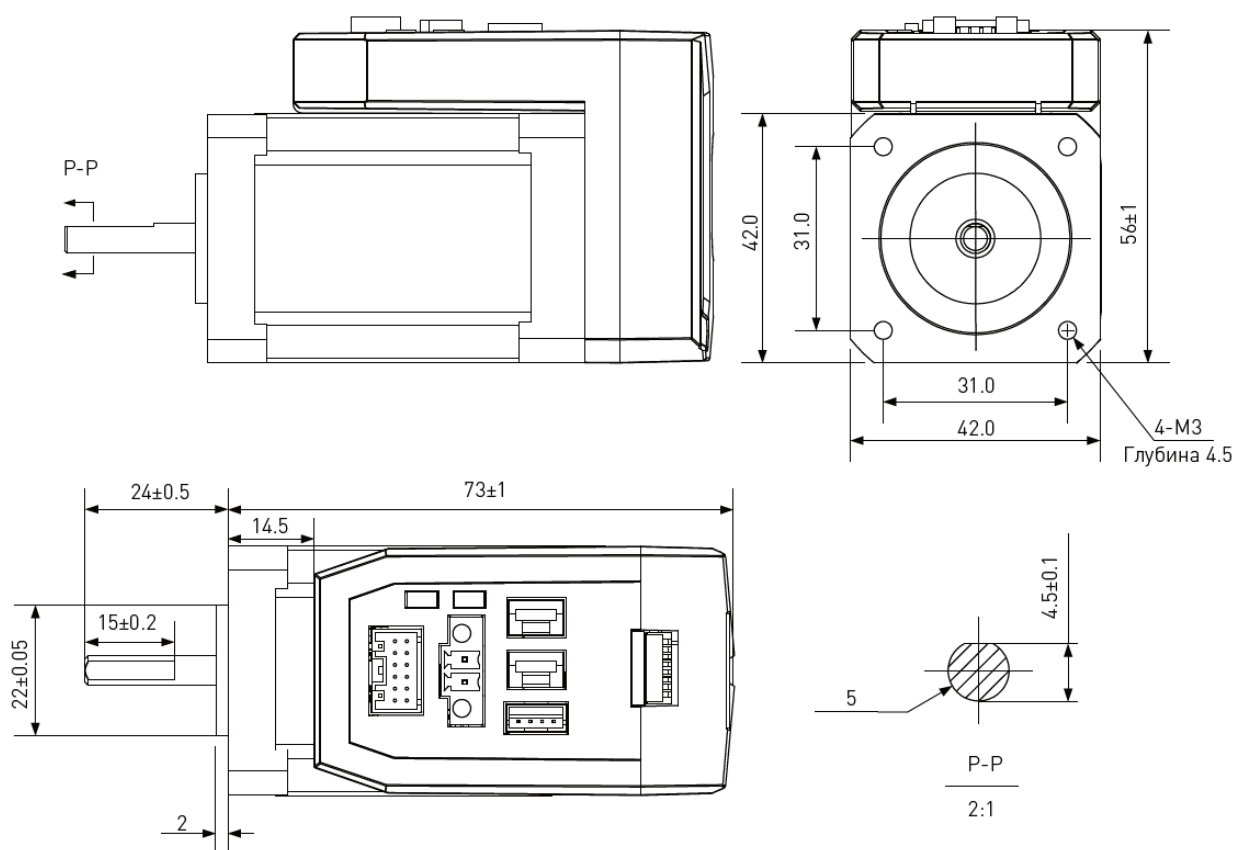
Габаритный чертеж привода iCS-RS1706.
